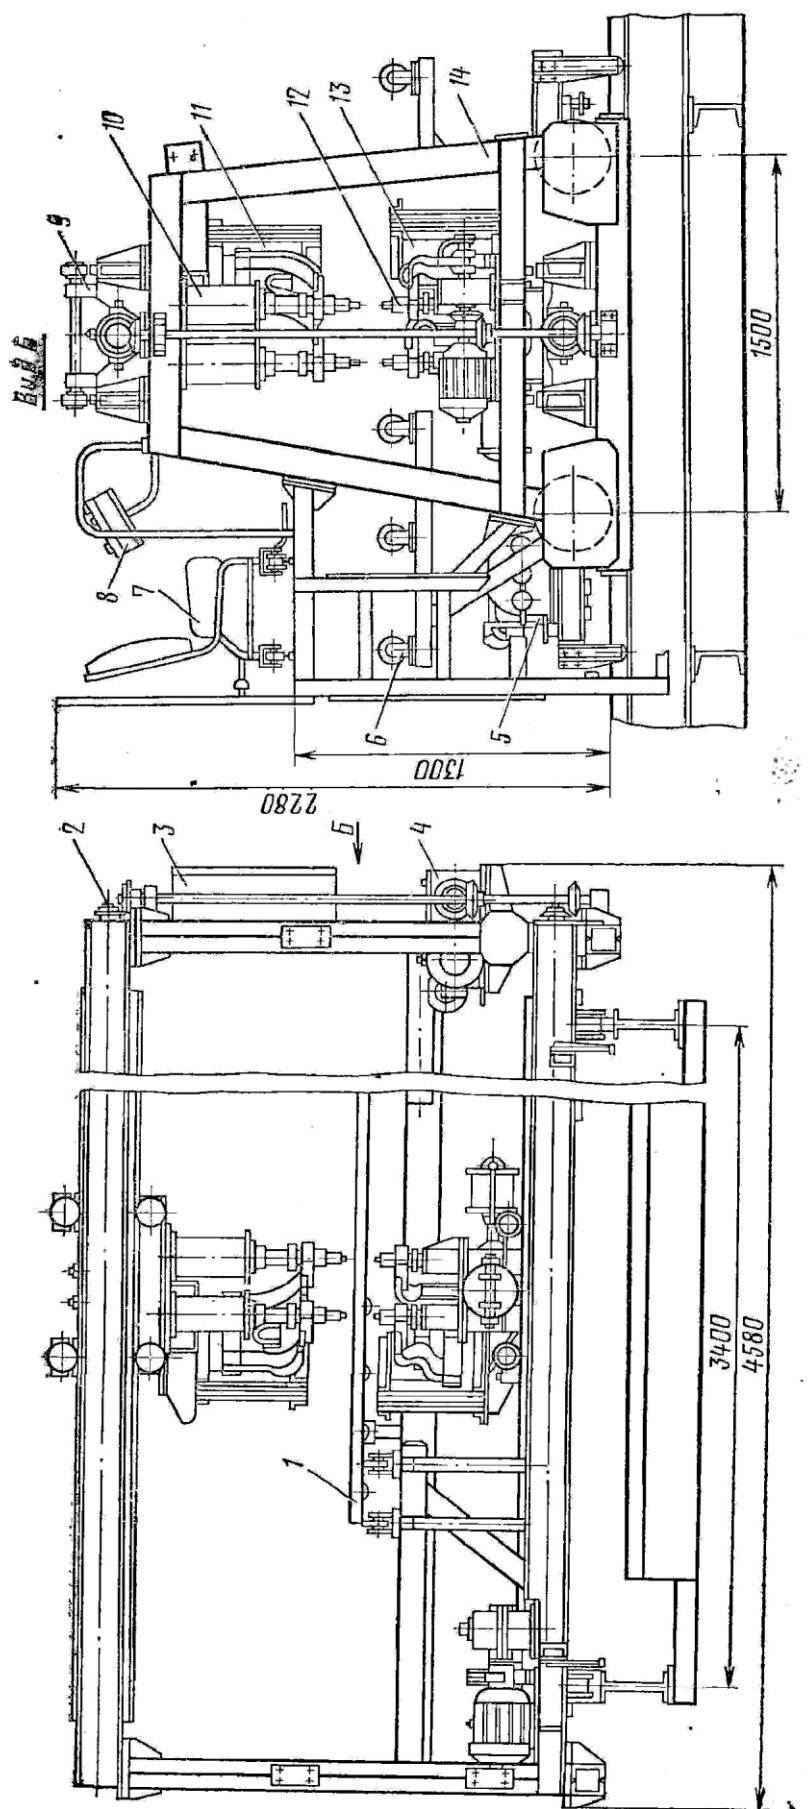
Установка порталного типа для контактной сварки боковых стен кузова с двусторонним подводом сварочного тока:
